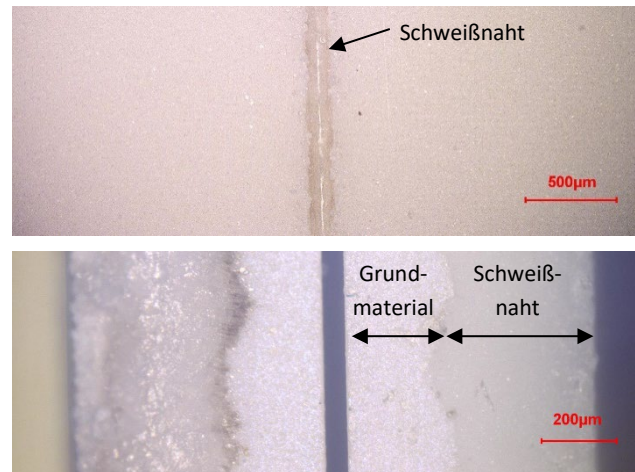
Erste Versuchsergebnisse zum Fügen von  $\text{Al}_2\text{O}_3$ -Keramik mittels UKP-Laserschweißprozess (oben: Draufsicht auf die Schweißnaht, unten: Bruchbild der Schweißnaht entlang der Fügezone).
